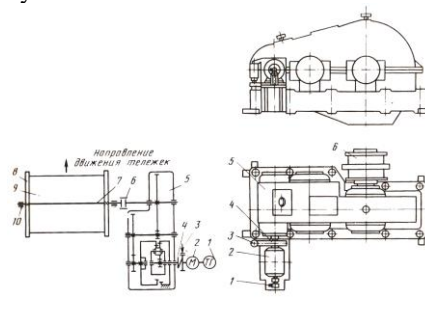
а) кінематична схема привода аглострічки; б) загальний вид привода стрічки агломашини
